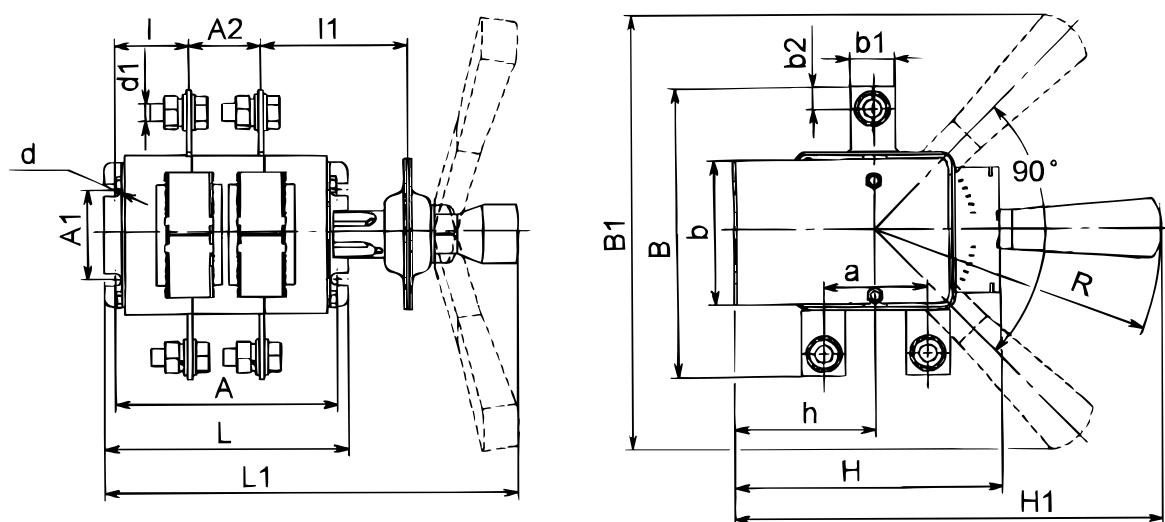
Выключатель-разъединитель на два направления двухполюсный с боковой смещенной рукояткой
